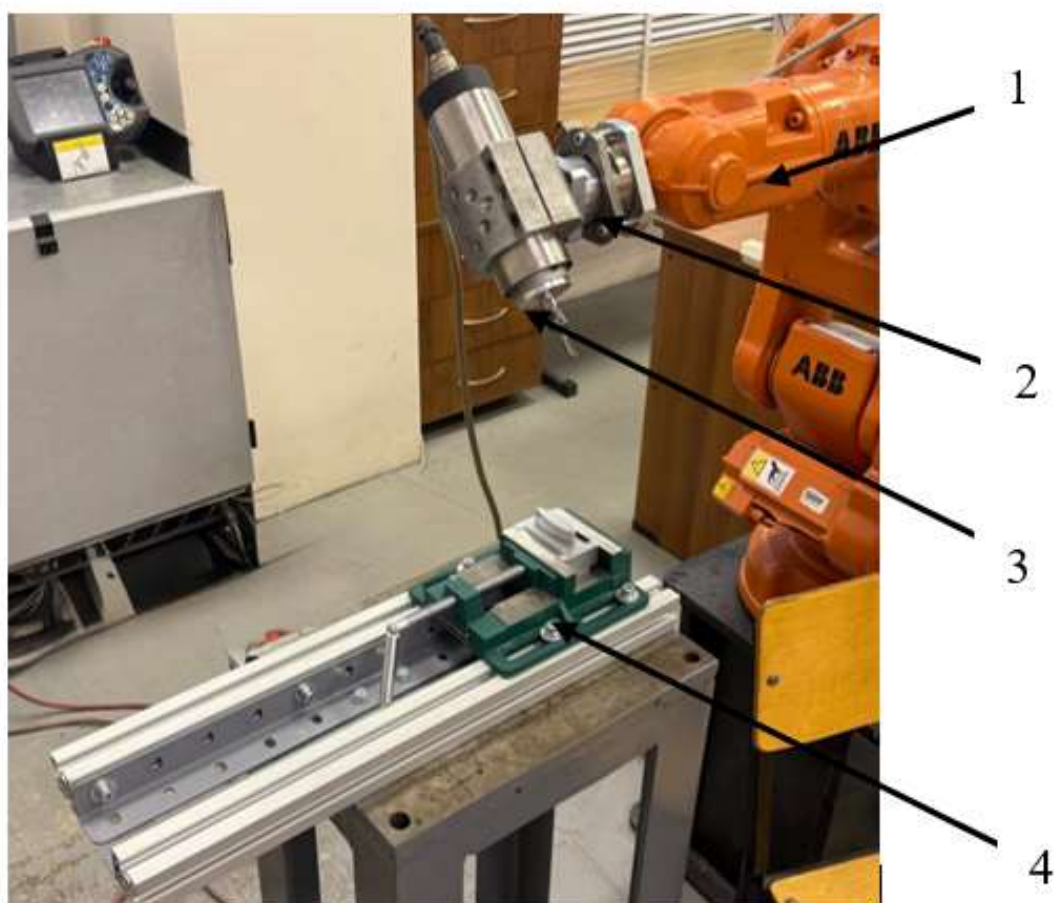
Экспериментальная установка для исследования роботизированной обработки: 1 – робот ABB IRB 140T; 2 – силомоментный датчик FTN – AXIA80 SI500-20 Ethernet; 3 – шпиндель GDF65-24000-0.8кВт; 4 – приспособление с установленной заготовкой
